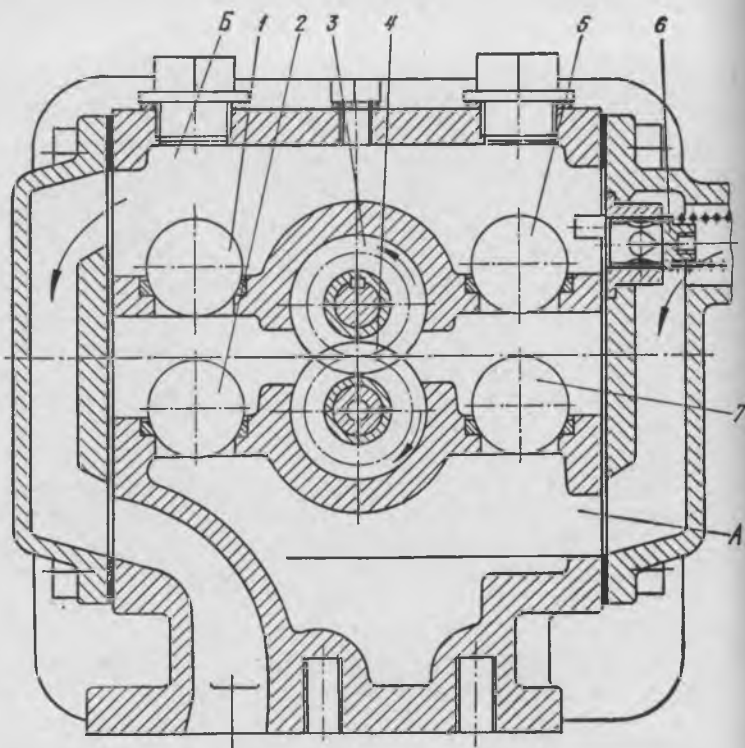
Шестеренчатый реверсивный насос дизеля NVD-36.
